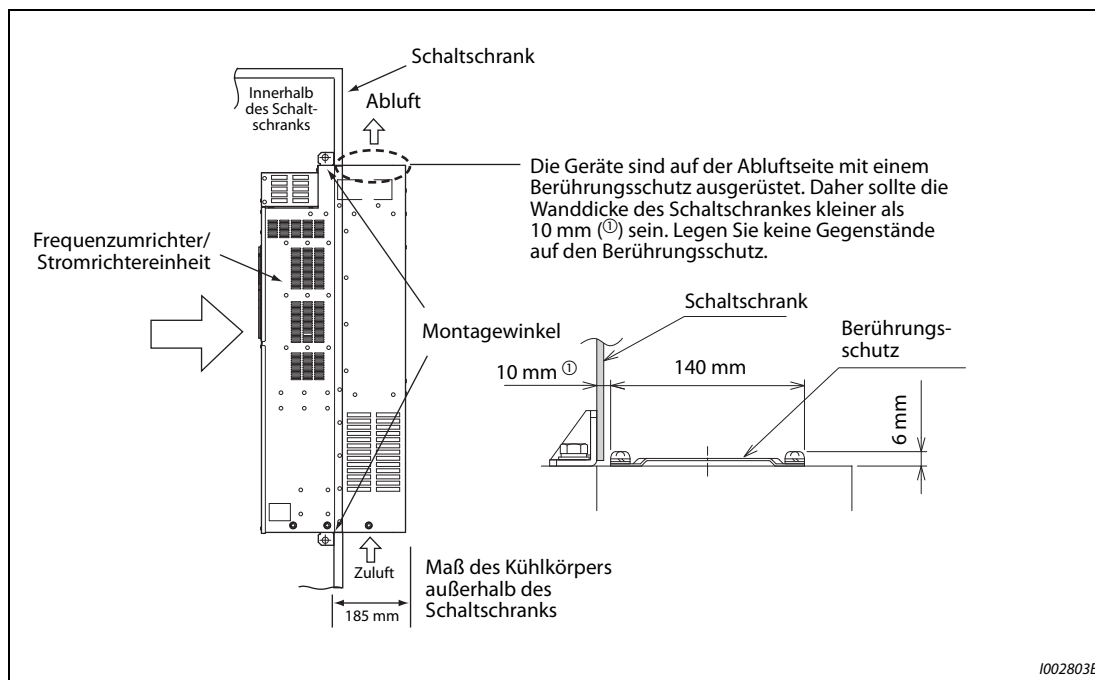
Montage des Frequenzumrichters zur externen Kühlluftführung
